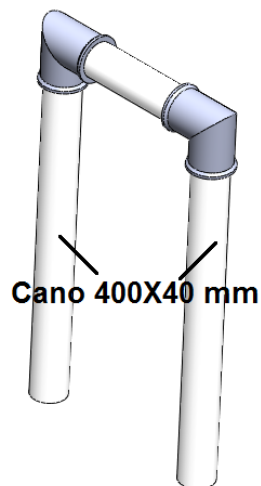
Montagem dos módulos – Módulo 3 – Passo 2
